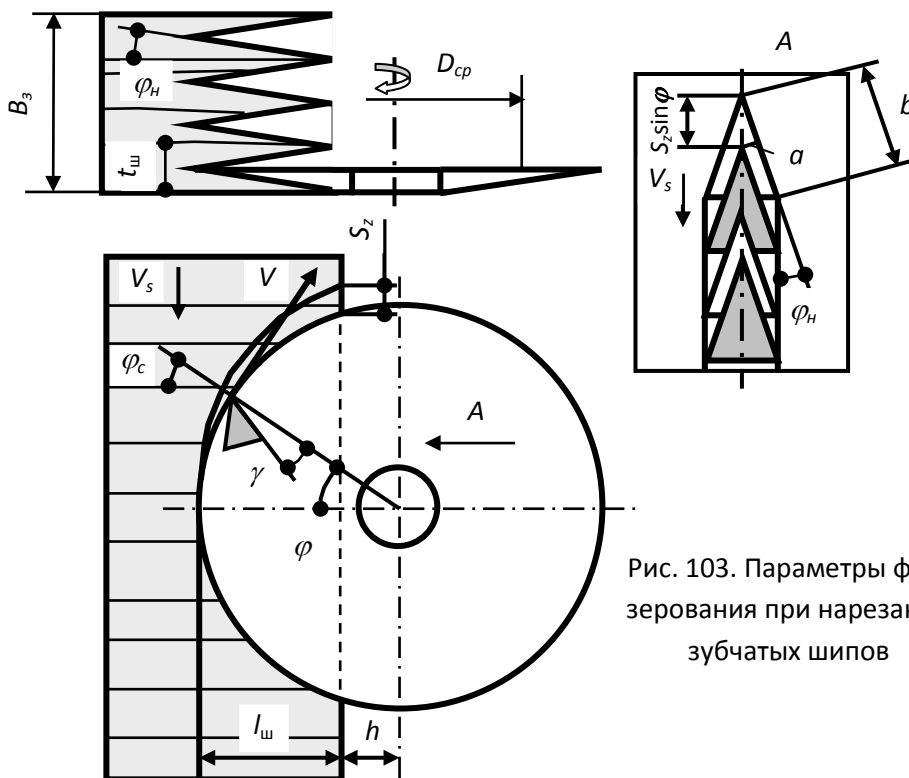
Параметры фрезерования при нарезании зубчатых шипов
